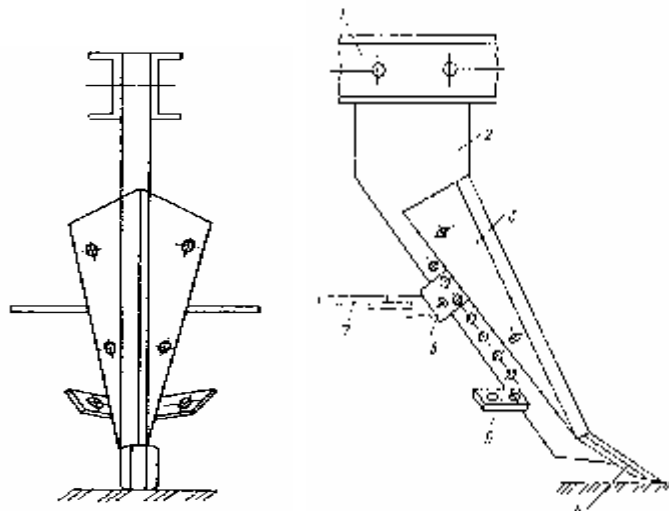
Рабочий орган глубокорыхлителя чизельного типа ГНЧ – 0.6
